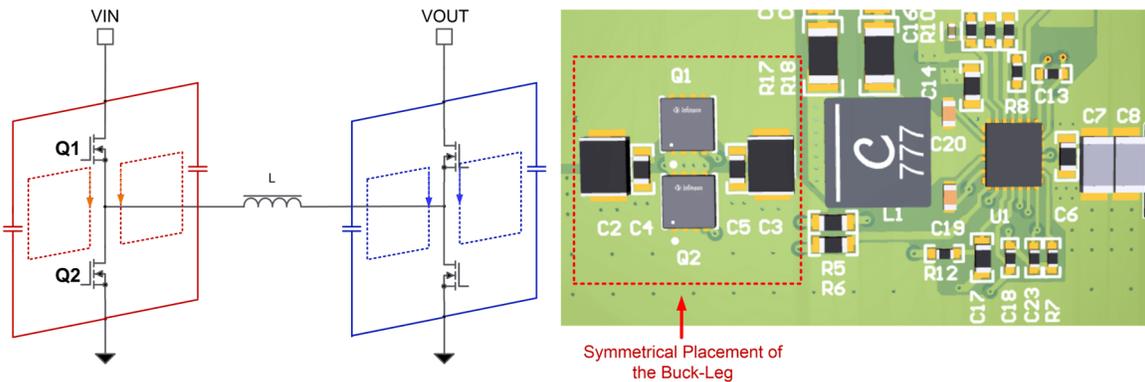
TPS55288 buck-부스트 컨버터의 대칭 PCB 배치
